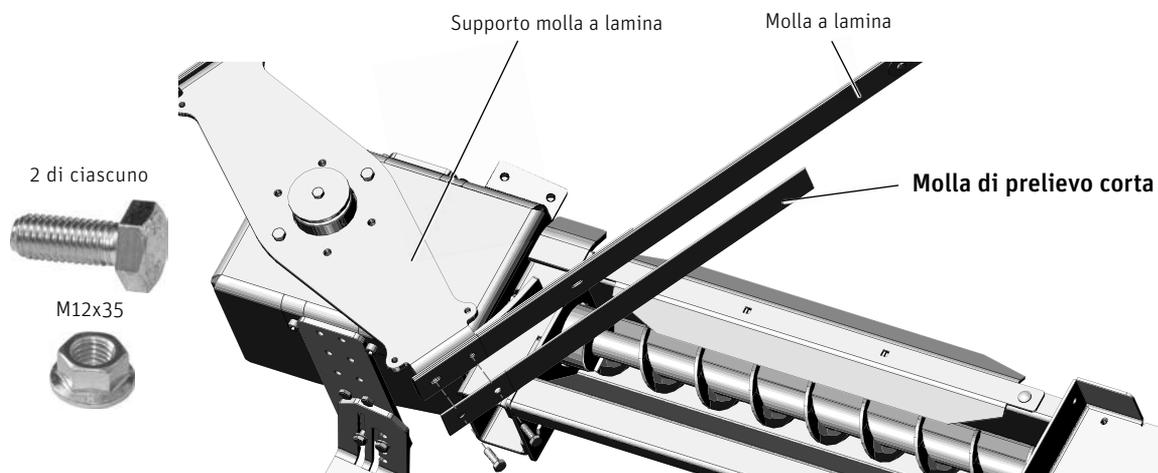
Montare la molla a lamina, avvitandola insieme alla molla di prelievo corta su un lato esterno
